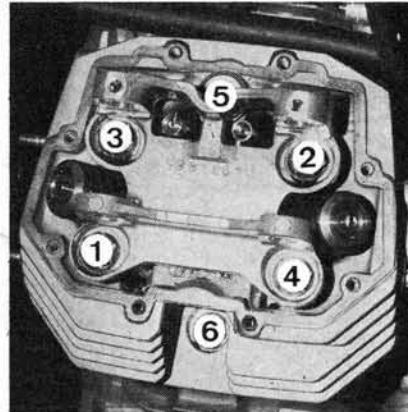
Ordre de serrage des fixations de culasse (Photo RMT)
